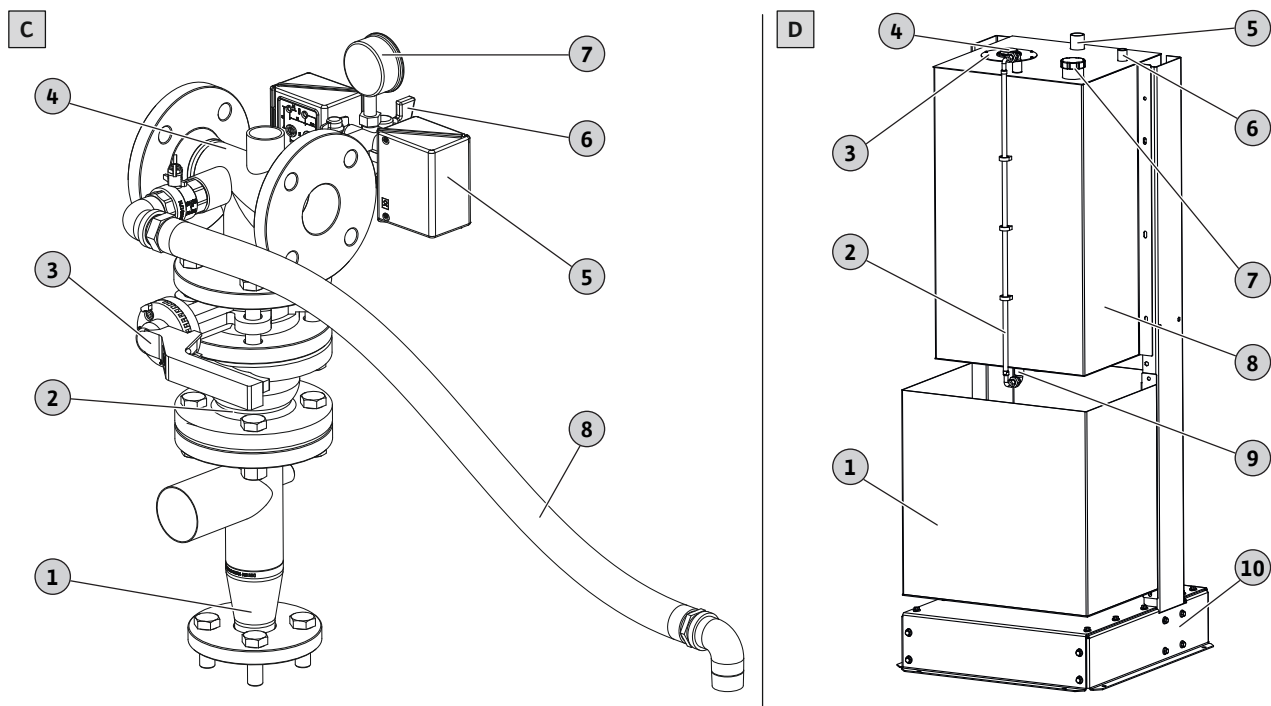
Конструкция нагнетателен изход и резервоар за гориво
